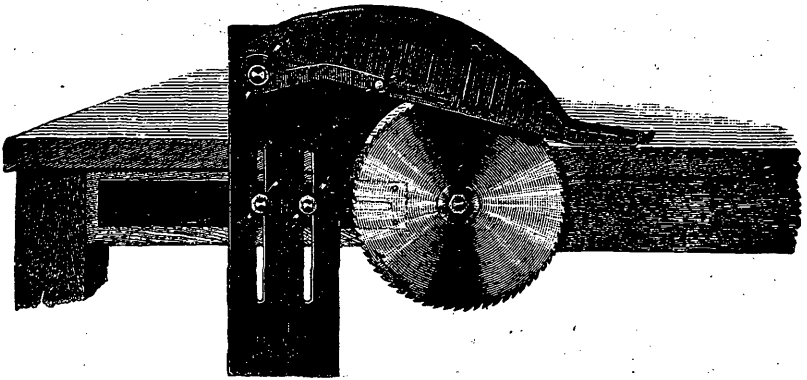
Caperuza de sierra de platillo, y cuchilla separadora, de la Maschinenbau-Anstalt Kirchner und Co.
